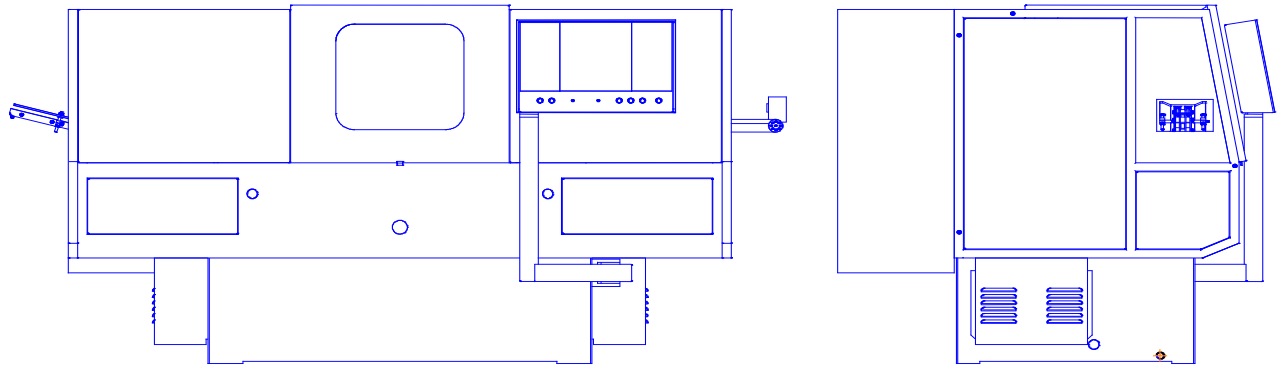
Загальний вид верстата токарного двошпиндельного
